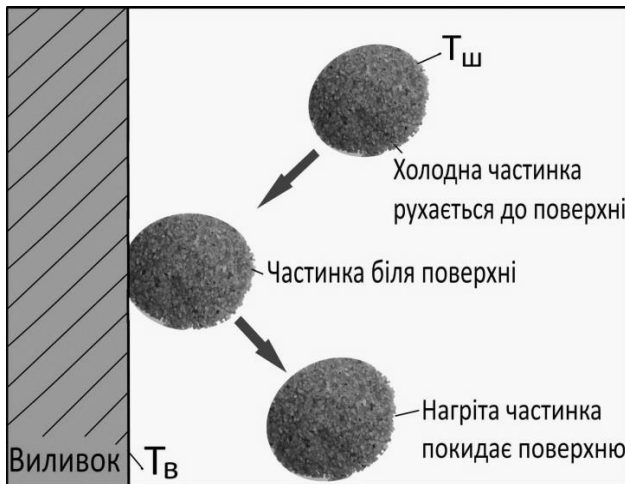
Схема руху частинок ФМ біля поверхні виливка
